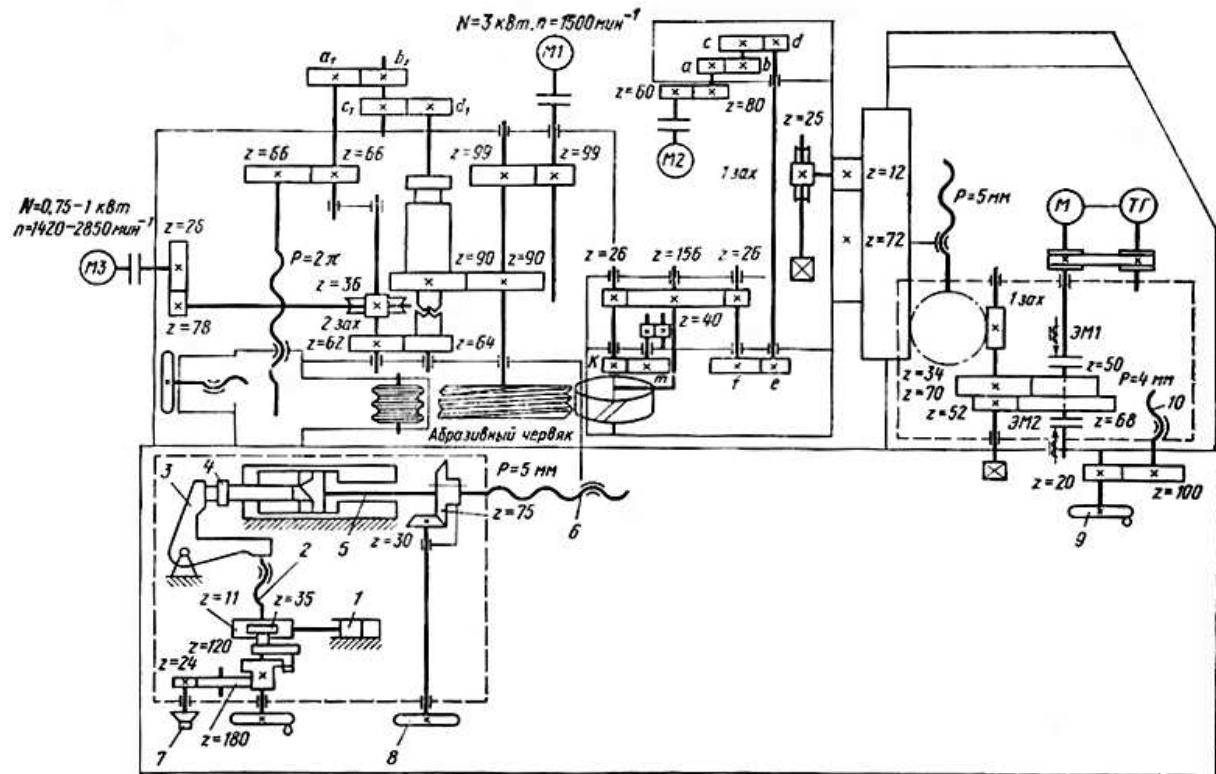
Кинематическая схема зубошлифовального станка модели 5B833
